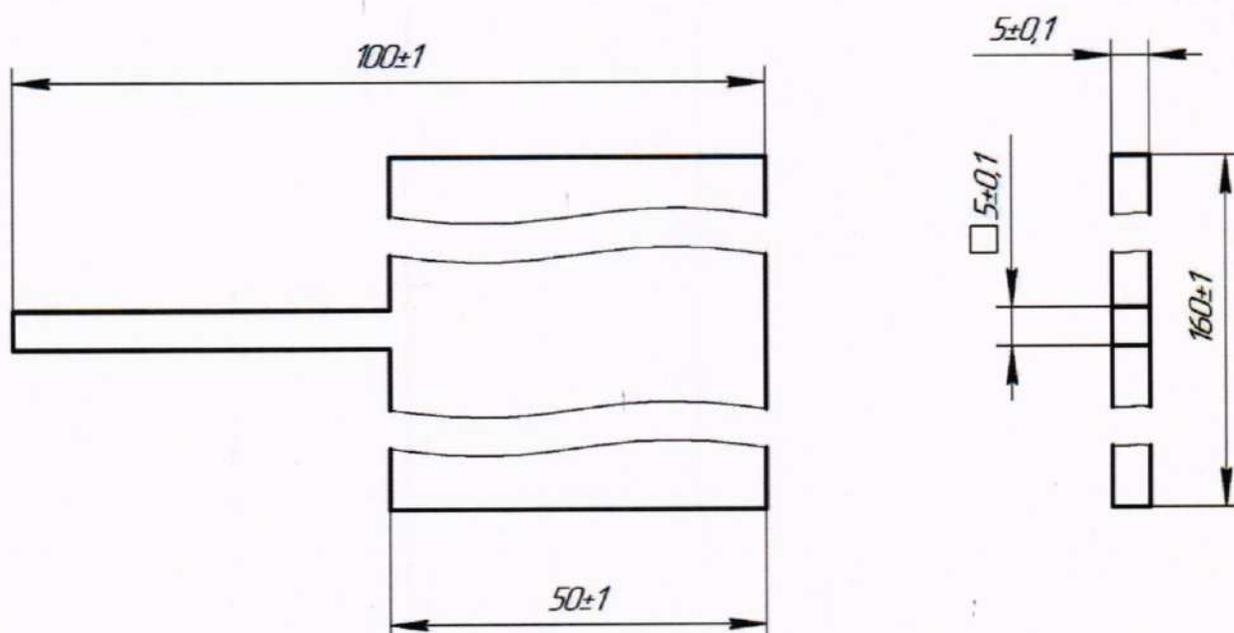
Чертеж оснастки для определения погрешности измерений угла поворота
